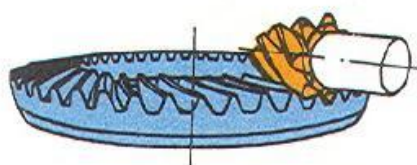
čelné súkolesie so zakrivenými zubami [22]
